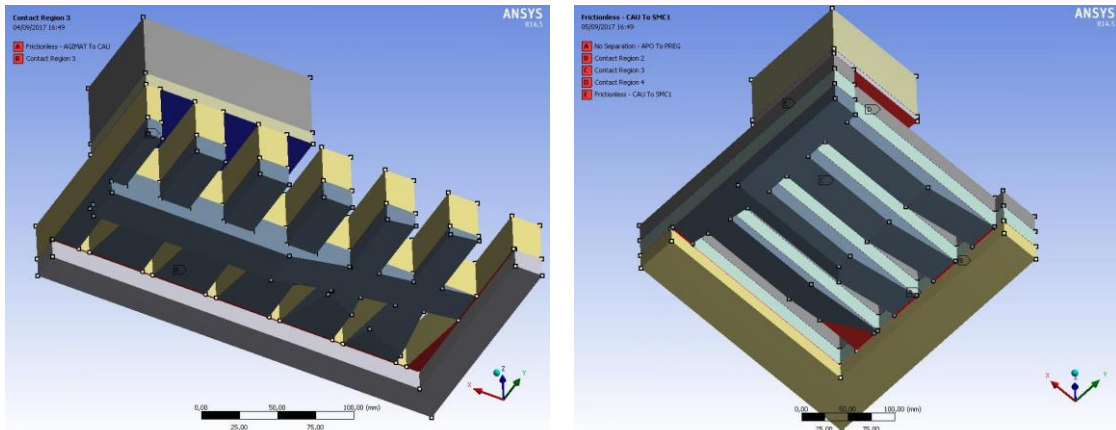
Contactos entre los componentes del molde C250 (izquierda) y del modelo D400 (derecha).
